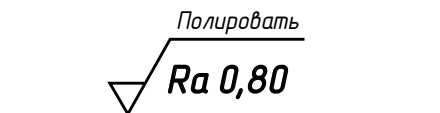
Обозначение шероховатости в случае, когда способ обработки является единственным
